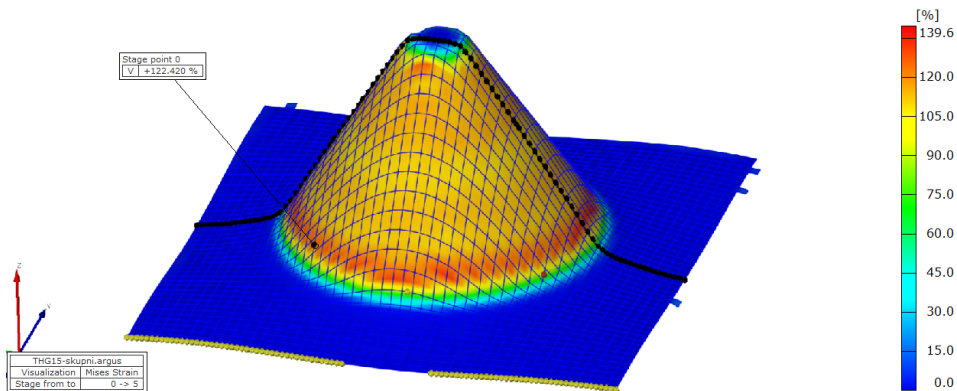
Krnji stožac materijal TH415, kut od 58° drugi stadij obrade, visina od 15 mm
